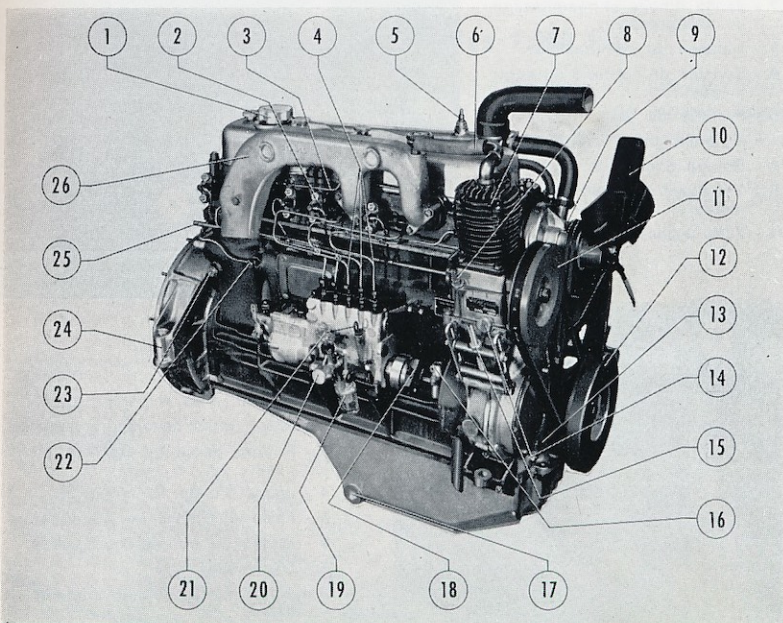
Vue d'ensemble 3/4 droit du moteur 5 cylindres.
